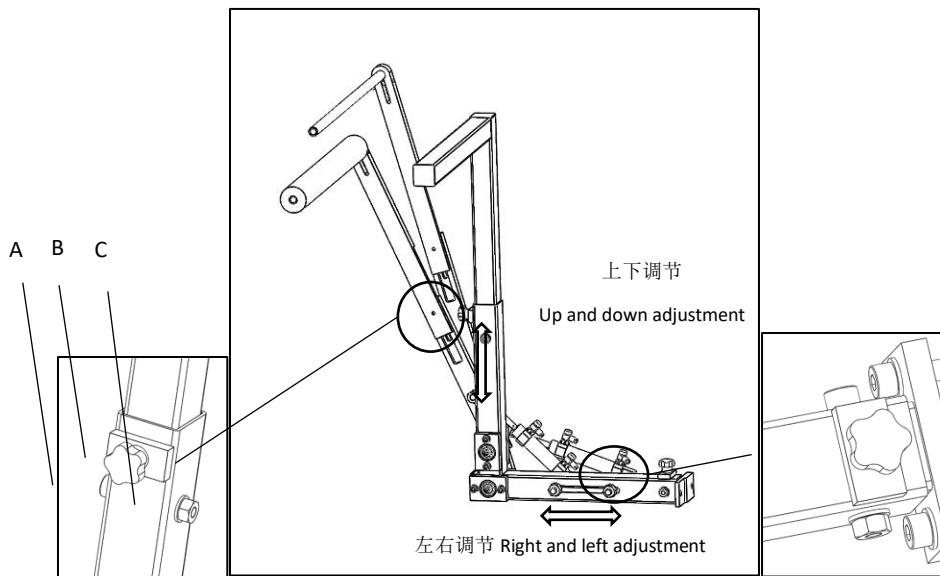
收料机构图 Figure 7.2 Collecting MechanismDrawing
